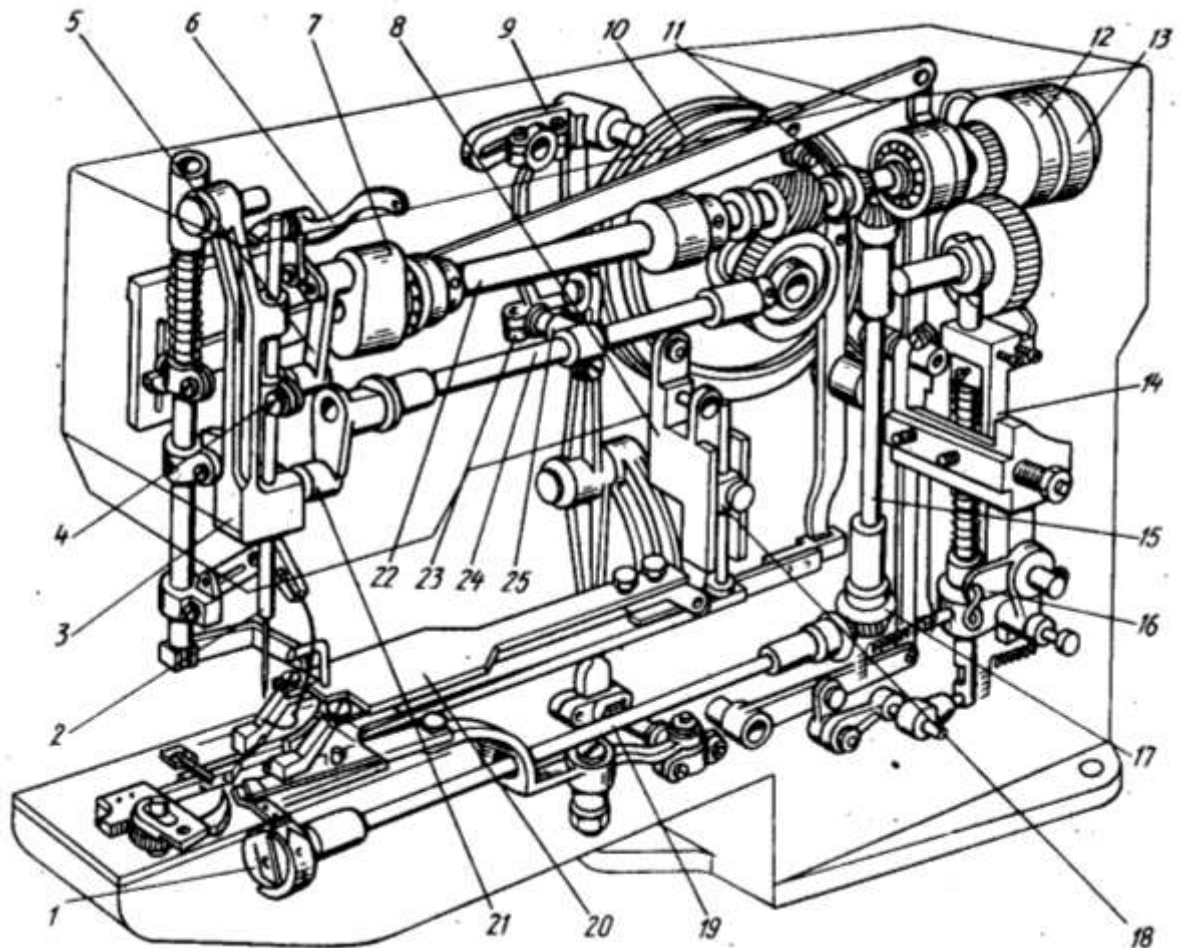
Конструктивно-кінематична схема машини напівавтомата для пришивання фурнітури
